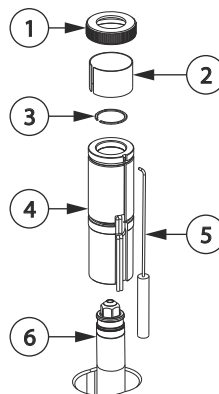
Conjunto de resistencia de la boquilla de cobre
